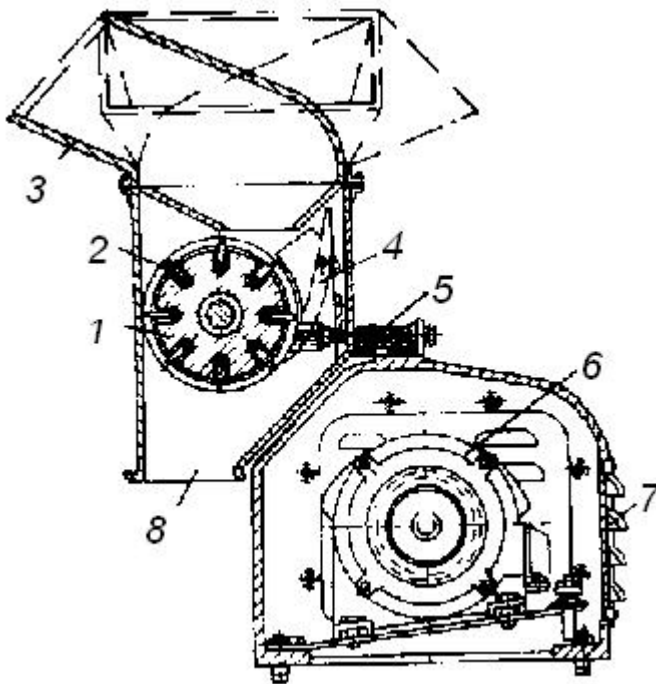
Дробилка для овощей и фруктов КДП-4:
